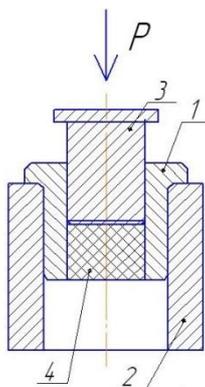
Схема проведения испытаний с приспособление в сборе (1 – матрица; 2 – обойма; 3 – шток (пуансон); 4 – опытный композит; P – сдвигающая нагрузка)
